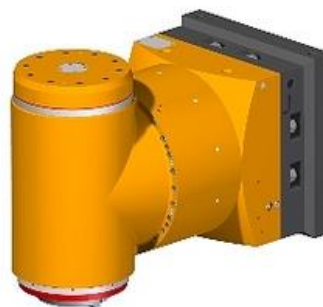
Různé konstrukční provedení frézovacích hlav od firmy FPT [2]
